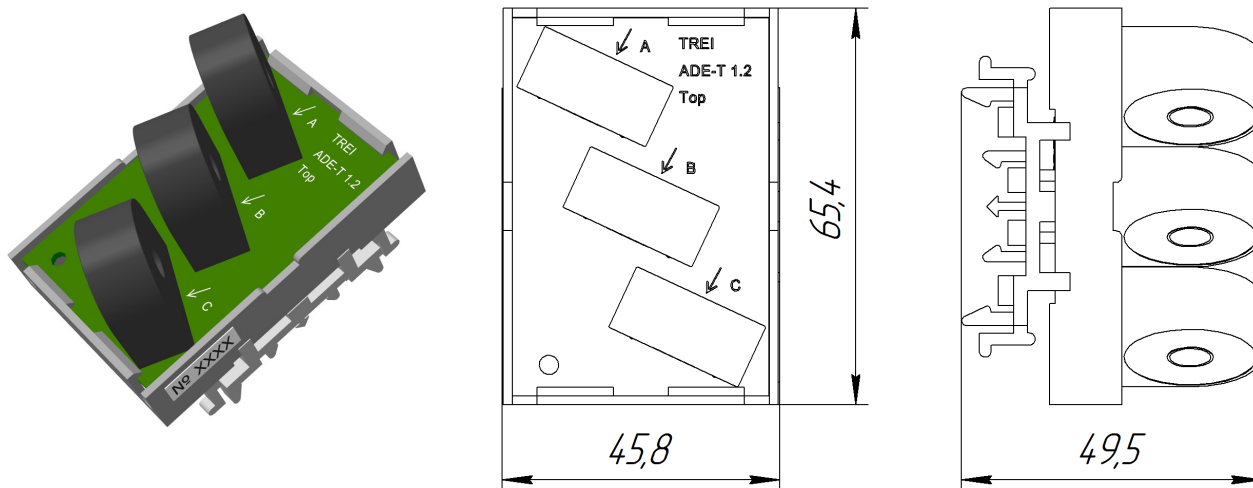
Общий вид и габаритные размеры блока M1071N-T
